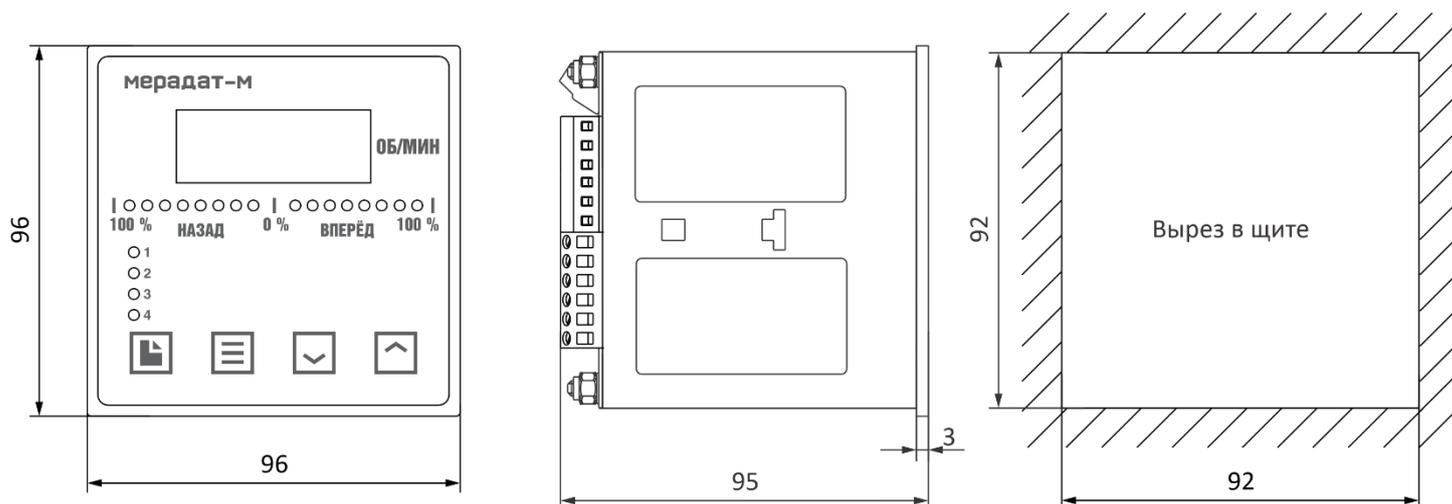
Габаритные размеры основного блока и блока индикации
